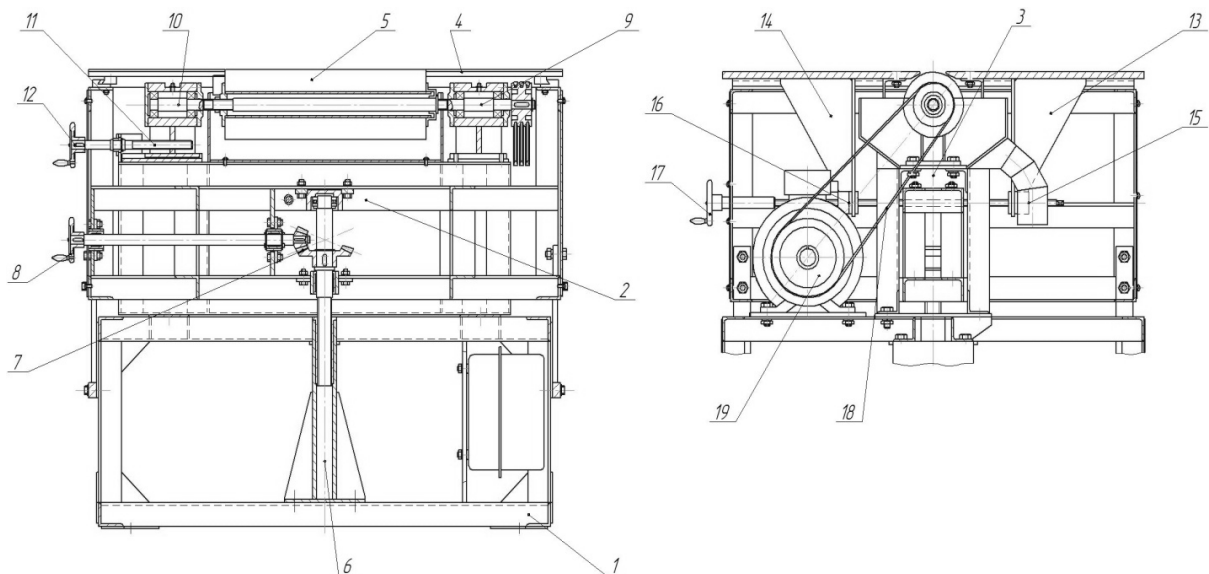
Переносна машина для очищення: 1 – нерухома рама; 2 – рухома рама; 3 – рама щіткового вала; 4 – стіл; 5 – щітковий вал; 6 – опора; 7 – конічна передача; 8, 12, 17 – штурвал; 9 – нерухома опора; 10 – рухома опора; 11 – гвинтова передача; 13, 14 – кронштейн; 15, 16 – втулка; 18 – клинопасова передача; 19 – електродвигун
